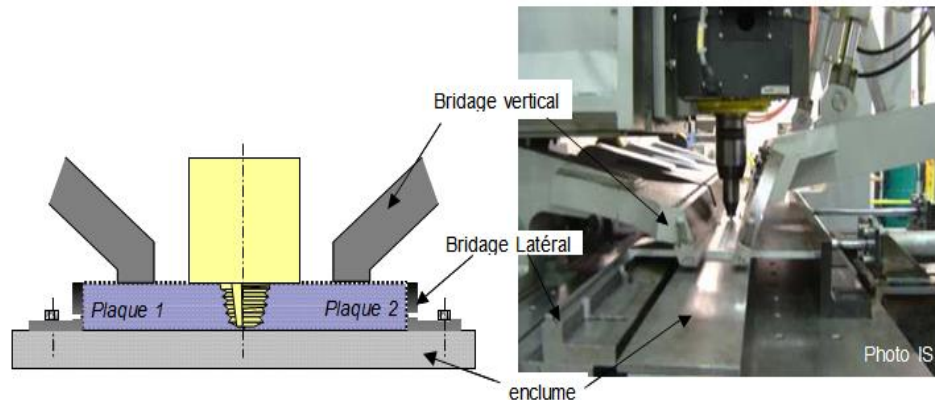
Système de bridage en soudage FSW [51].
